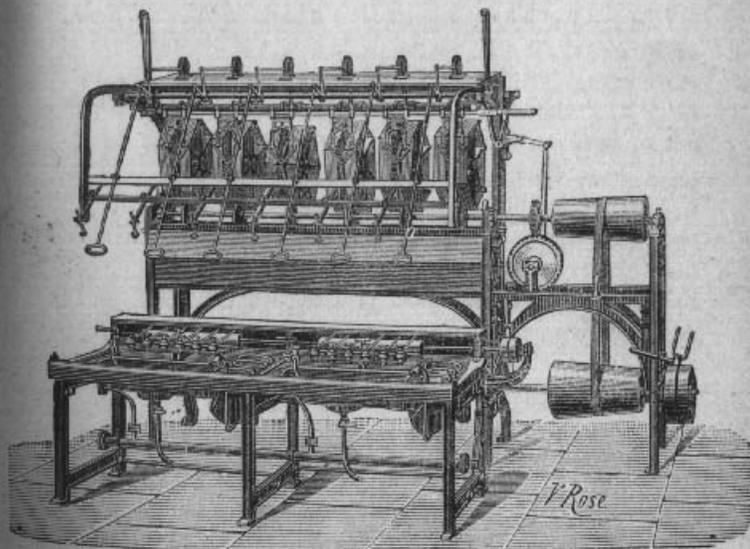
Appareil à filer la soie à deux bassines, système Léon Camel, construit par les chantiers de la Buire à Lyon.
